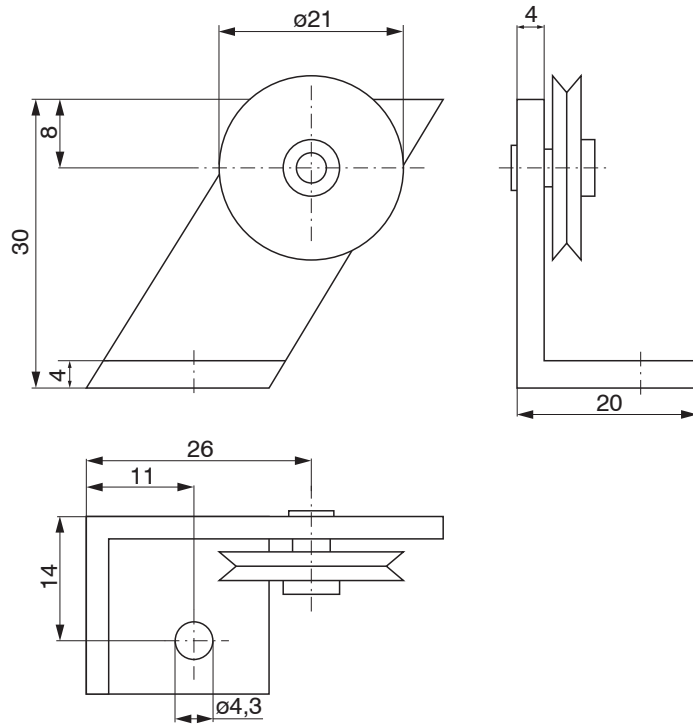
Umlenkrolle TR3-WDS mit Montagefuß, Abmessungen in mm, nicht maßstabgetreu
